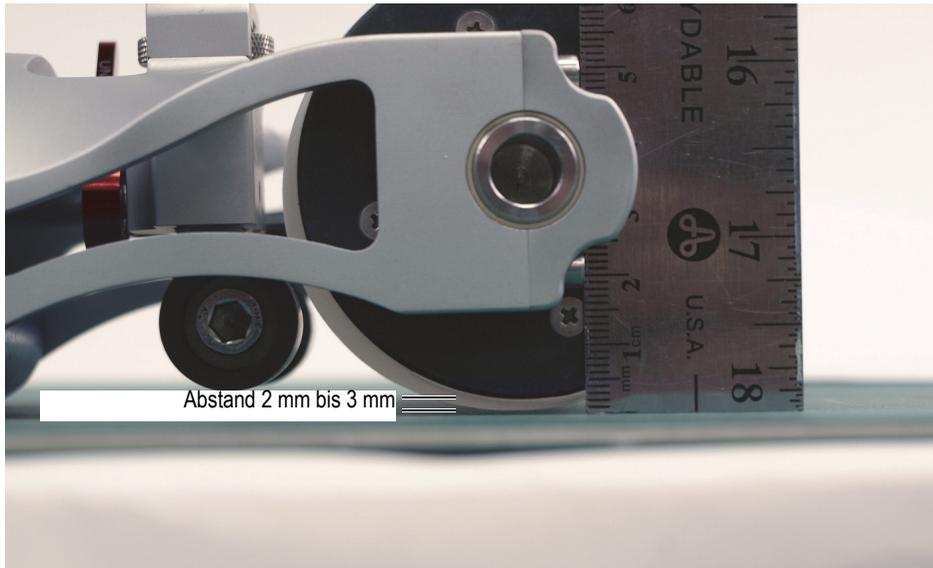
Abstand zwischen Flansch der Akustikrolle und Prüffläche (RollerFORM)
